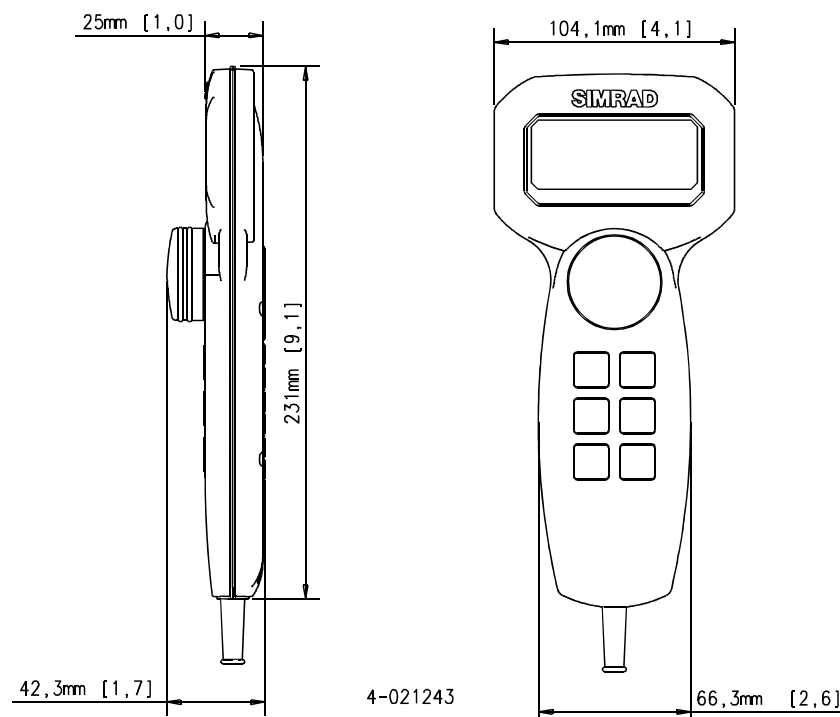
Dimensiones de la Unidad de Control AP50
